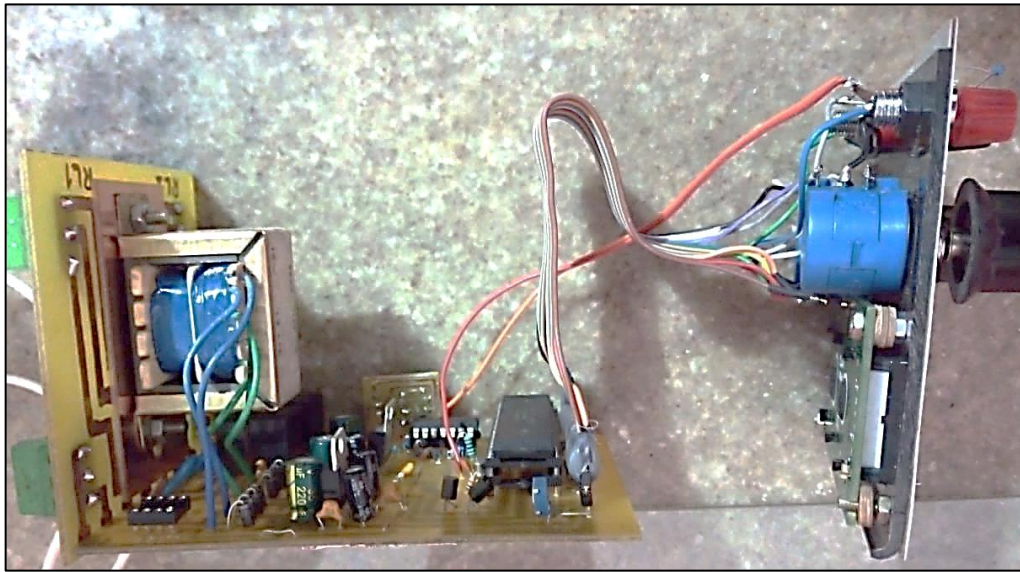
INÍCIO DO PROCESSO DE SOLDAGEM DOS COMPONENTES – PLACA 1/2
